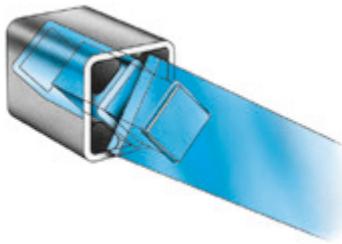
Steckverbindungen: Innenvierkant aus Stahlrohr, Hebelarm mit aufgeschweisstem Vierkantprofil
